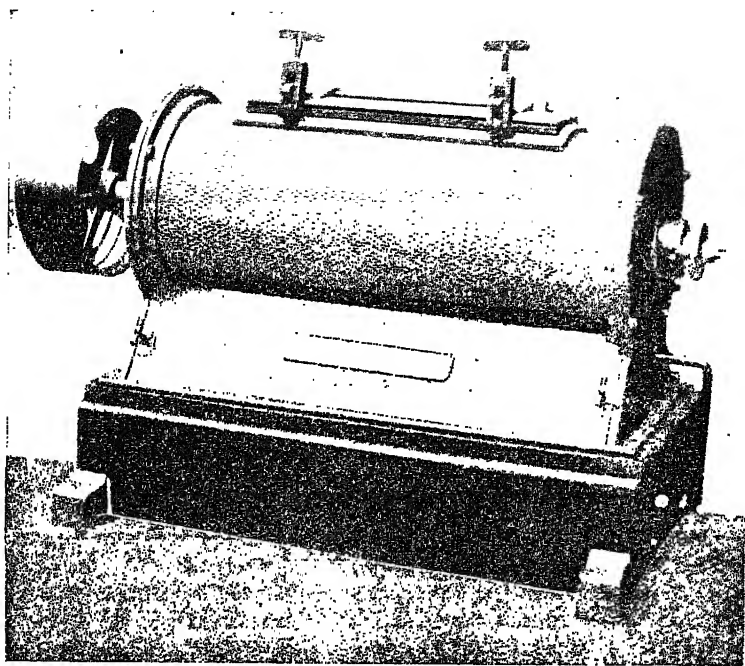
Machine à polir ou « brillanteuse » pour la fabrication de la poudre d'aluminium (d'après L. Guillet).
